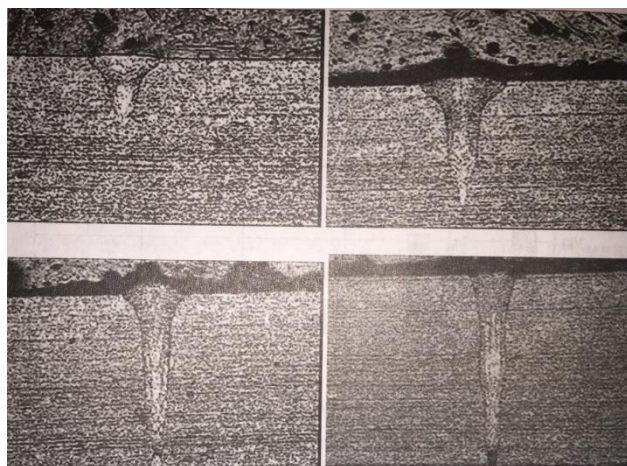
Сварные швы, выполненные одномодовым волоконным лазером мощностью 400 Вт (JK400FL); нержавеющая сталь марки 304SS, скорость сварки 9 м/мин; защитный газ-аргон: а-4,98 МВт/см<sup>2</sup>;
